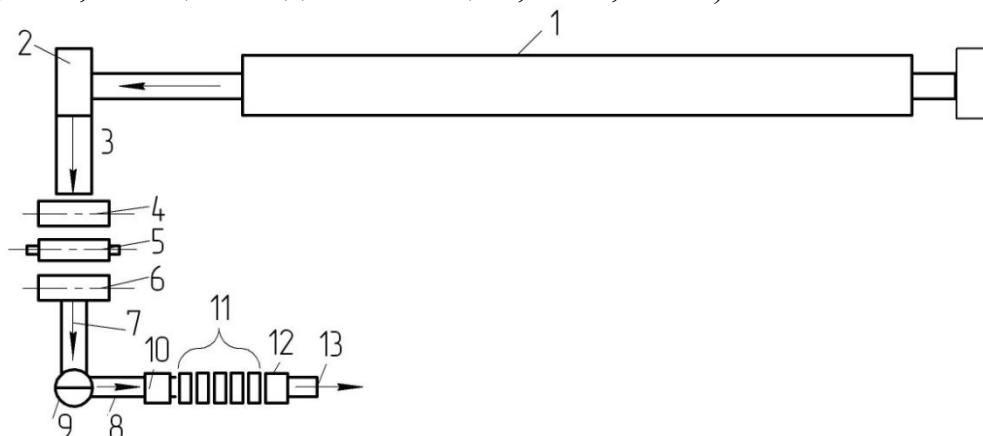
Схема розташування устаткування при виробництві холоднокатаних штаб з проміжним агрегатом (ППА) перемотування: 1-НТА; 2-роликів машина (моталка); 3-транс-портер; 4-розмотувач; 5-ролики, що тягнуть (прокатна кліть); 6-моталка; 7, 8-передавальні транспортери; 9-поворотний стіл; 10-розмотувач; 11-НСХП; 12-моталка; 13-прибиральний пристрій.
